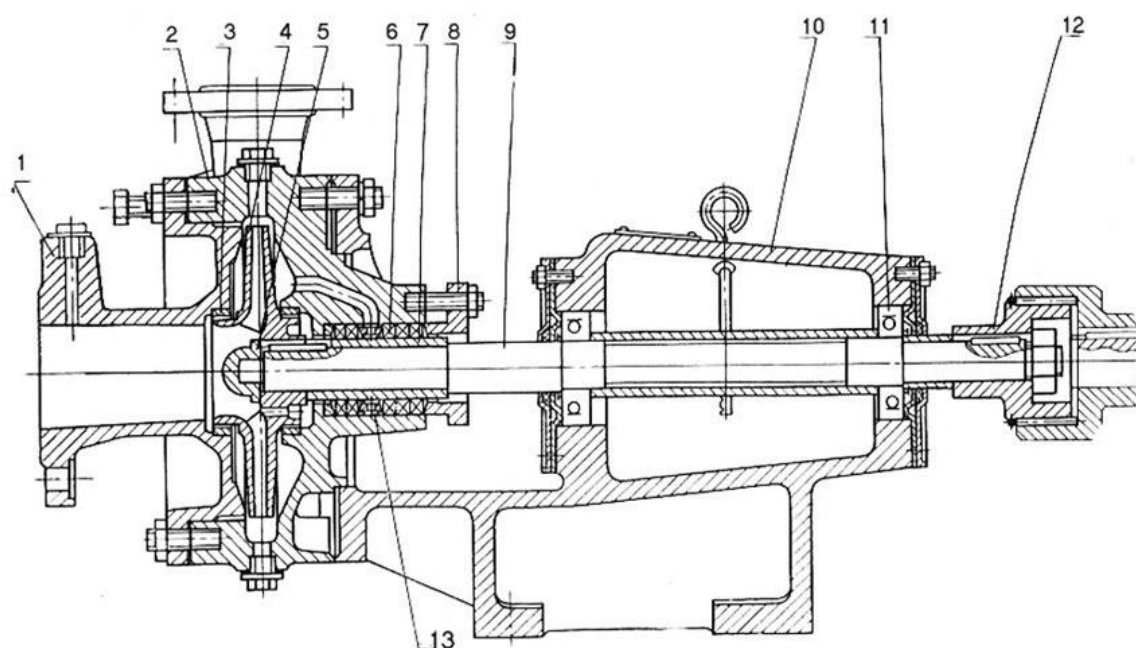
Конструкция насоса типа 3К: 1-крышка корпуса со всасывающим патрубком; 2-корпус; 3-кольцо уплотняющее; 4-рабочее колесо; 5-гайка рабочего колеса; 6-сальниковая набивка; 7-втулка защитная; 8-крышка сальника; 9-вал; 10-опорная стойка; 11-подшипник качения; 12-муфта; 13-втулка сальника.
